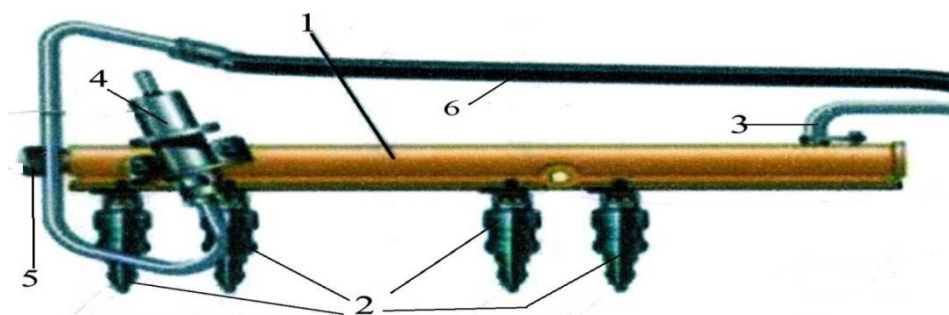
Схема устройства рампы: 1 – топливная рампа; 2 – электромагнитная форсунка; 3 – нагнетательный трубопровод; 4 – регулятор давления топлива; 5 – колпачок штуцера давления топлива; 6 – сливной трубопровод;
